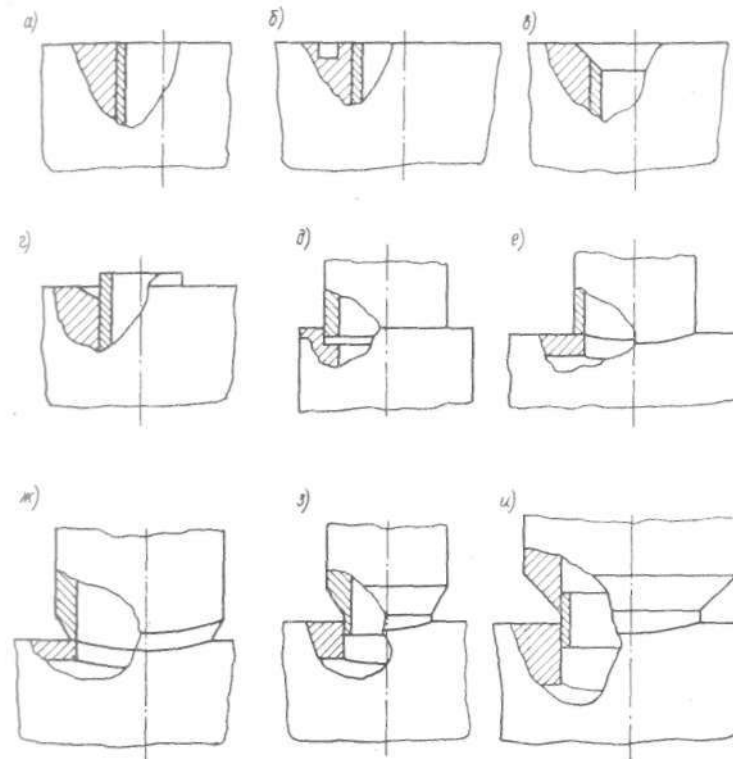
Типы угловых сварных соединений труб и трубных элементов.
